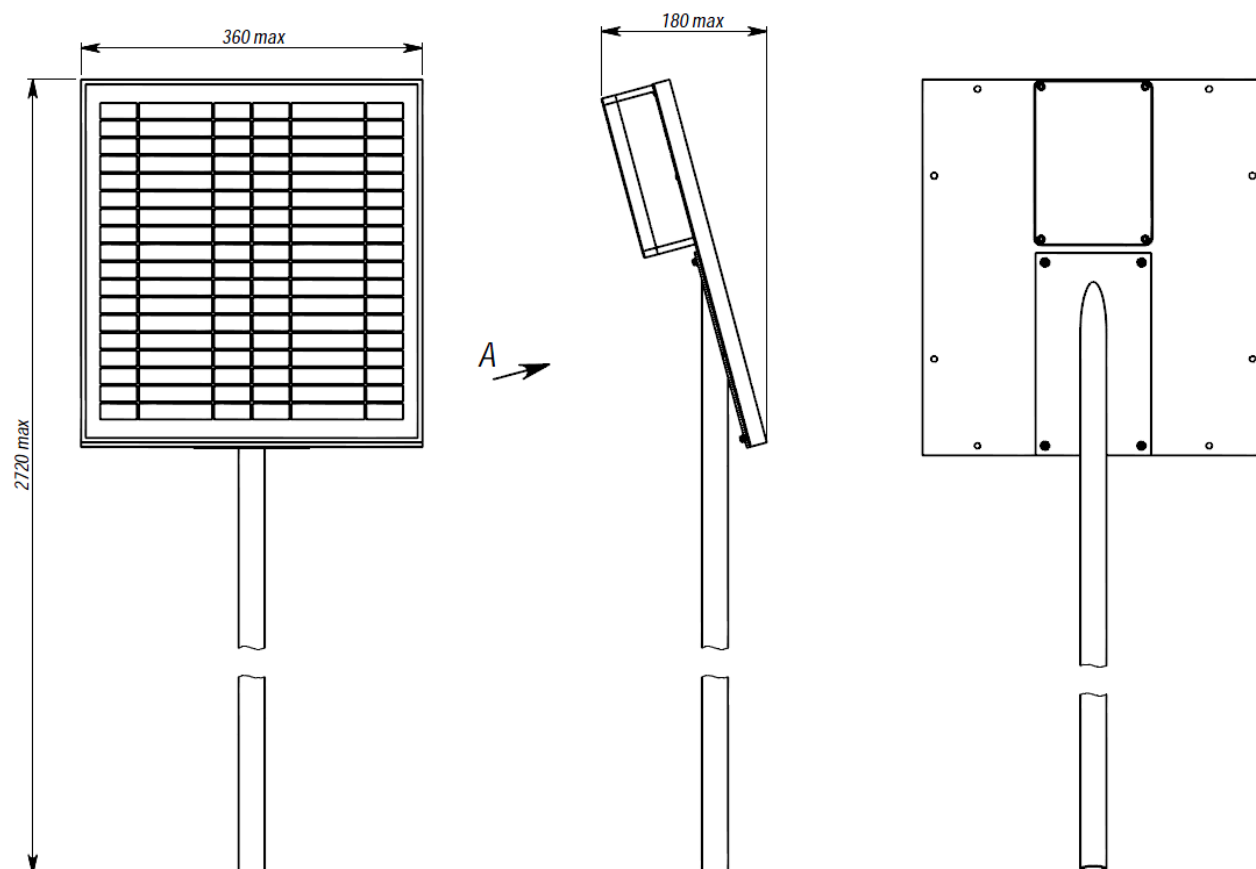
Вид и габаритные размеры сборки модуля Терминал-РТ1.1 с выносной стойкой
